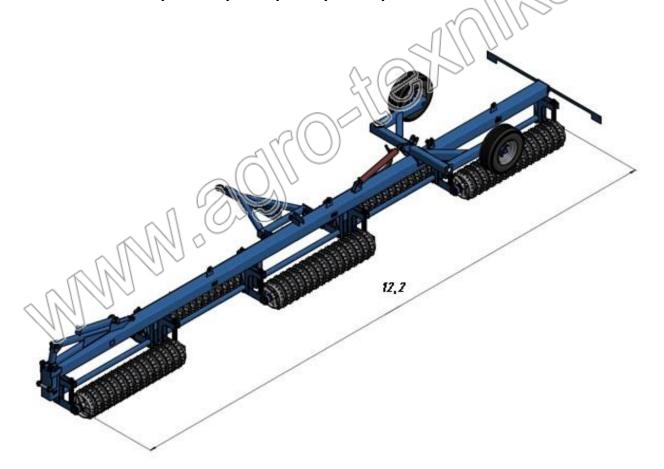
а Габаритные размеры в рабочем положении КЗК-12У.
